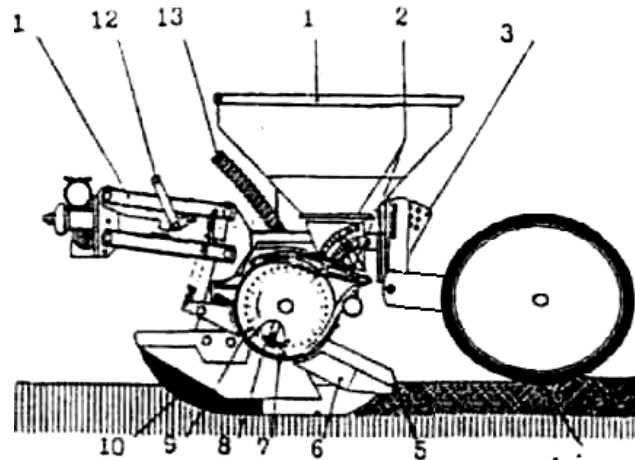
Посівна секція сівалки СТВ-8К для загортання насіння на глибину до 12 см: 1 – насіннева банка; 2 – відсікач насіння зі шкалою; 3 – регулятор глибини; 4 – опорно-прикочувальний коток; 5 – спорожнювальний клапан; 6 – загортач; 7 – скидач; 8 – ролик; 10 – сошник; 11 – підвіска; 12 – фіксатор підвіски; 13 – всмоктувальний шланг.
